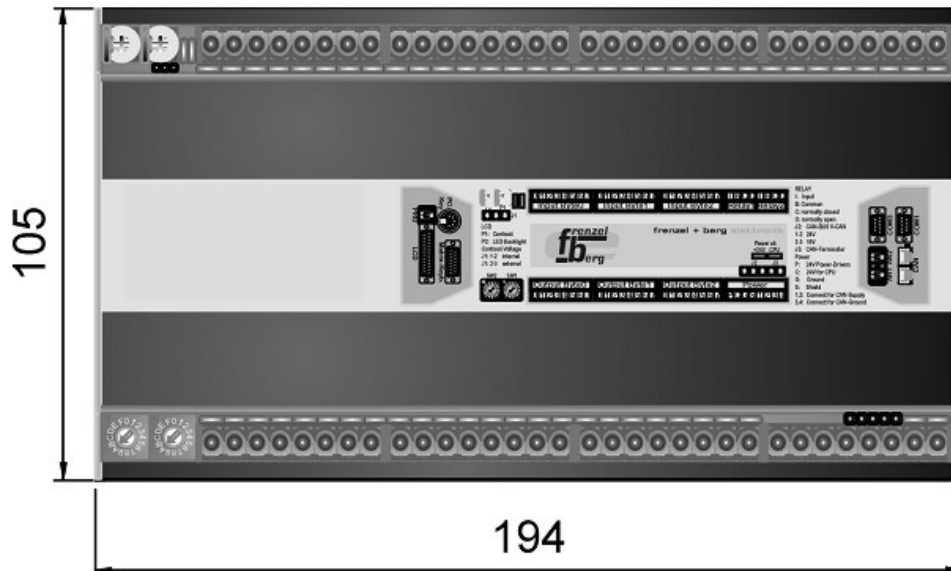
im Metallgehäuse – Frontal- und Seitenansicht
